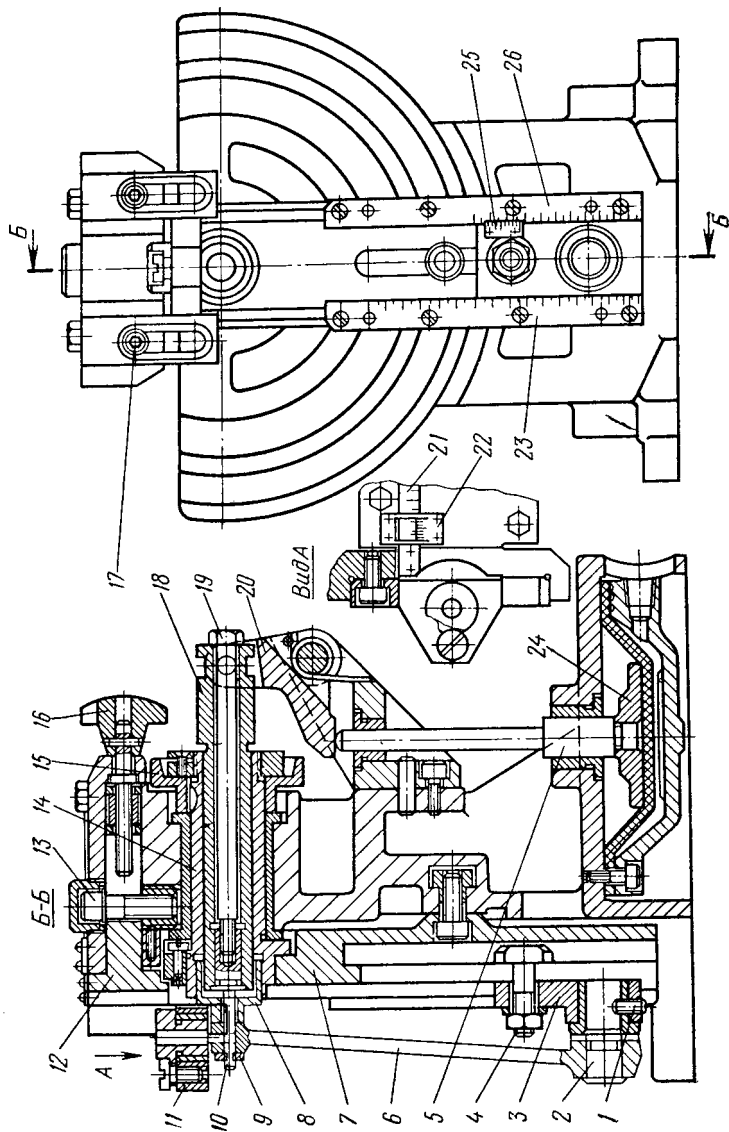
Универсально-наладочное приспособление для обработки отверстий в торце головки рычагов
